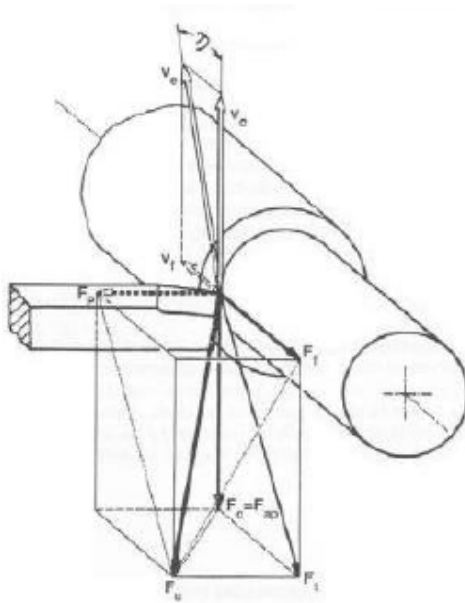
Direção das componentes da força de usinagem em torneamento.
